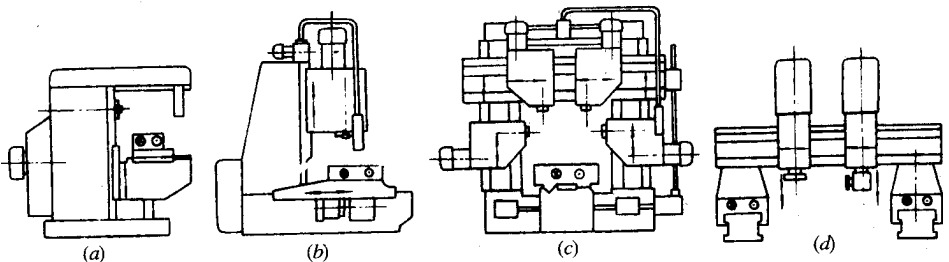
因工件尺寸和质量大小引起的铣床不同结构布局
